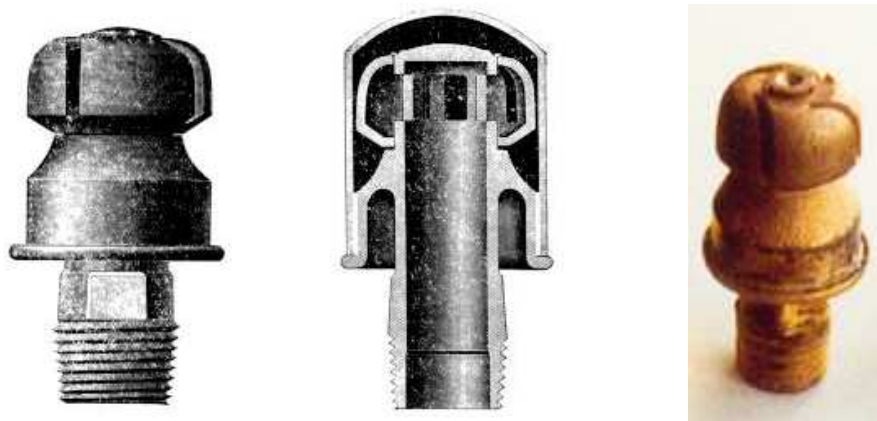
První Parmelleho sprinklerové zařízení z roku 1874 [17]
